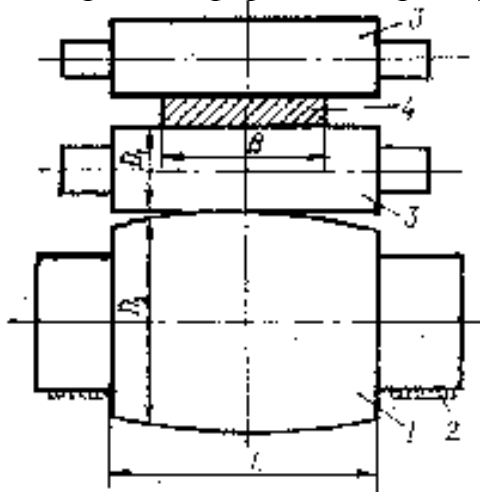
Модель кліті кварто: 1 – опорний валок; 2 – опори шийок валка; 3 – робочие валки; 4 – алюминиевая пластина
